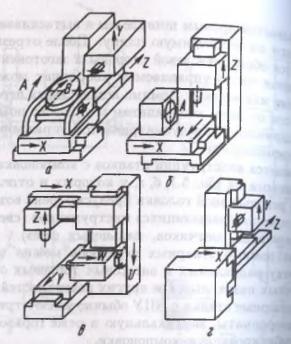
Разновидности компоновок сверлильнофрезерно-расточных станков с ЧПУ
